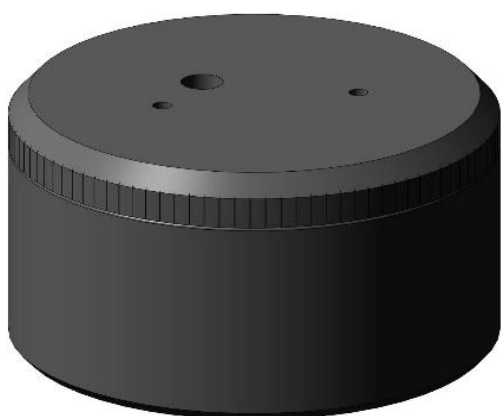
3D модель корпуса прессовой оснастки для прессования столбика во времязадающее кольцо ПИМа в сборе с двумя штифтами и кольцом
